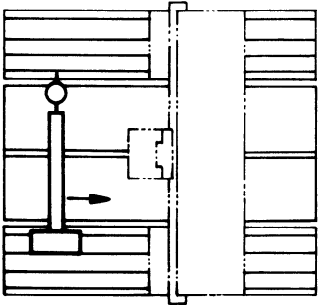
Type 3: Machine à deux têtes de fraisage sur traverse mobile
